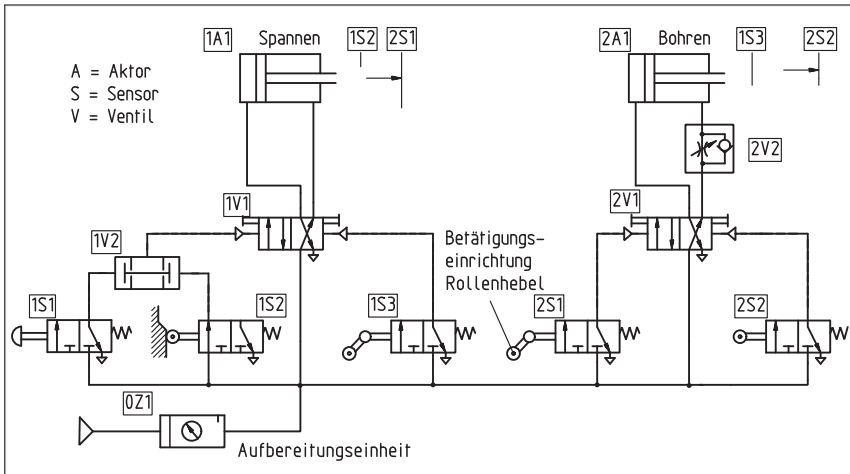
Schaltplan einer Bohreinrichtung
